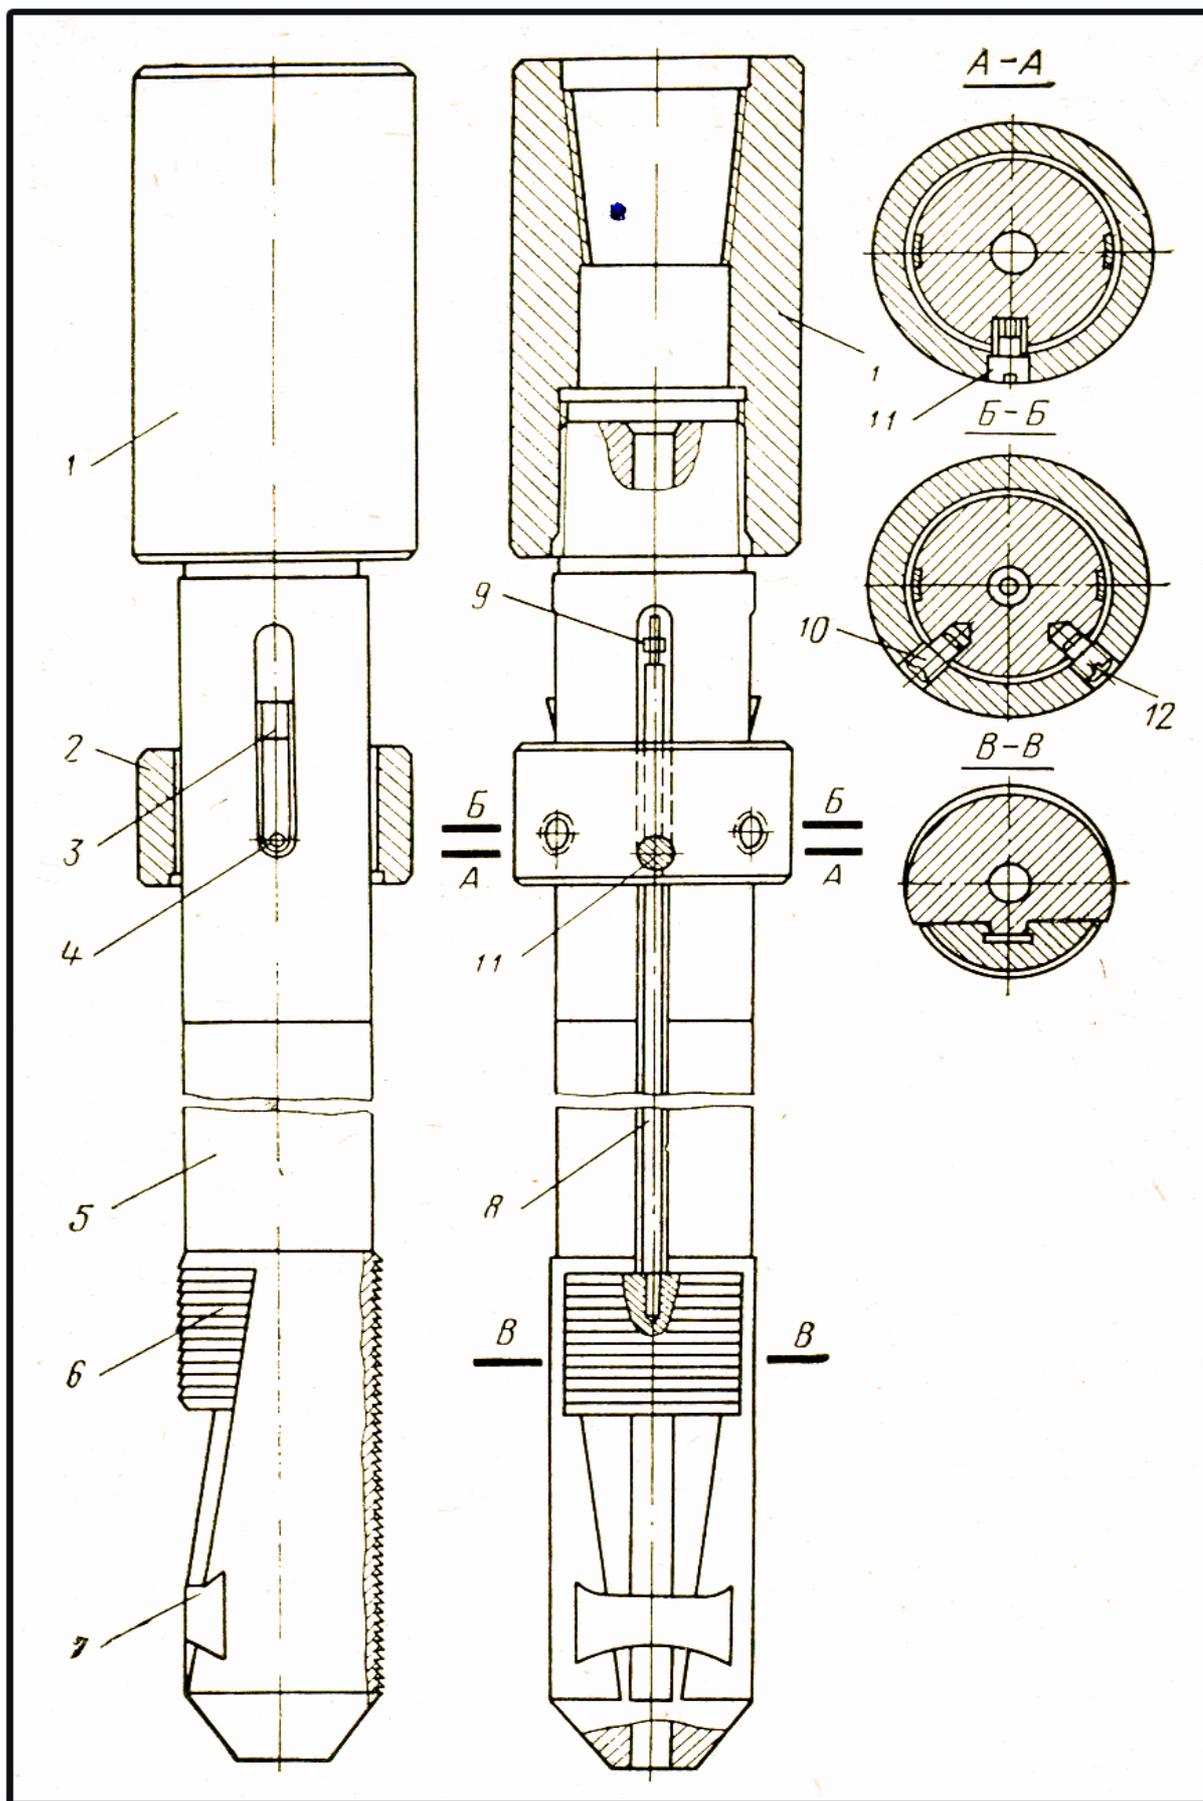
Внутренняя освобождающаяся трубоволка
